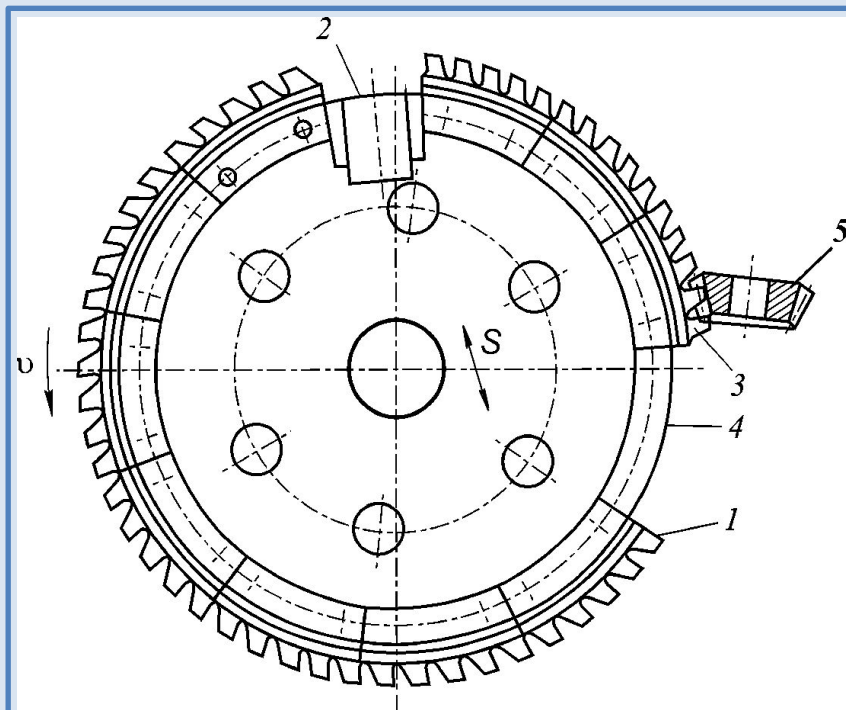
Схема нарезания конического прямозубого колеса круговой протяжкой:
